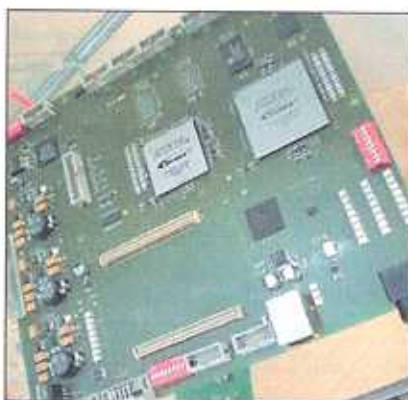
Typische Baugruppe, gefertigt bei Plath EFT
